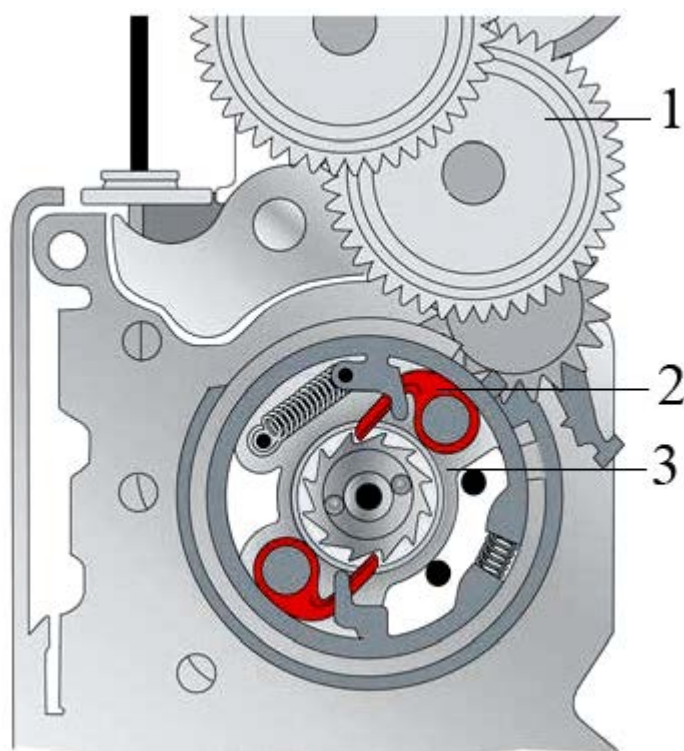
Ремень безопасности с реверсивным преднатяжителем: 1 – зубчатая передача; 2 – крюк; 3 – ведомый диск
